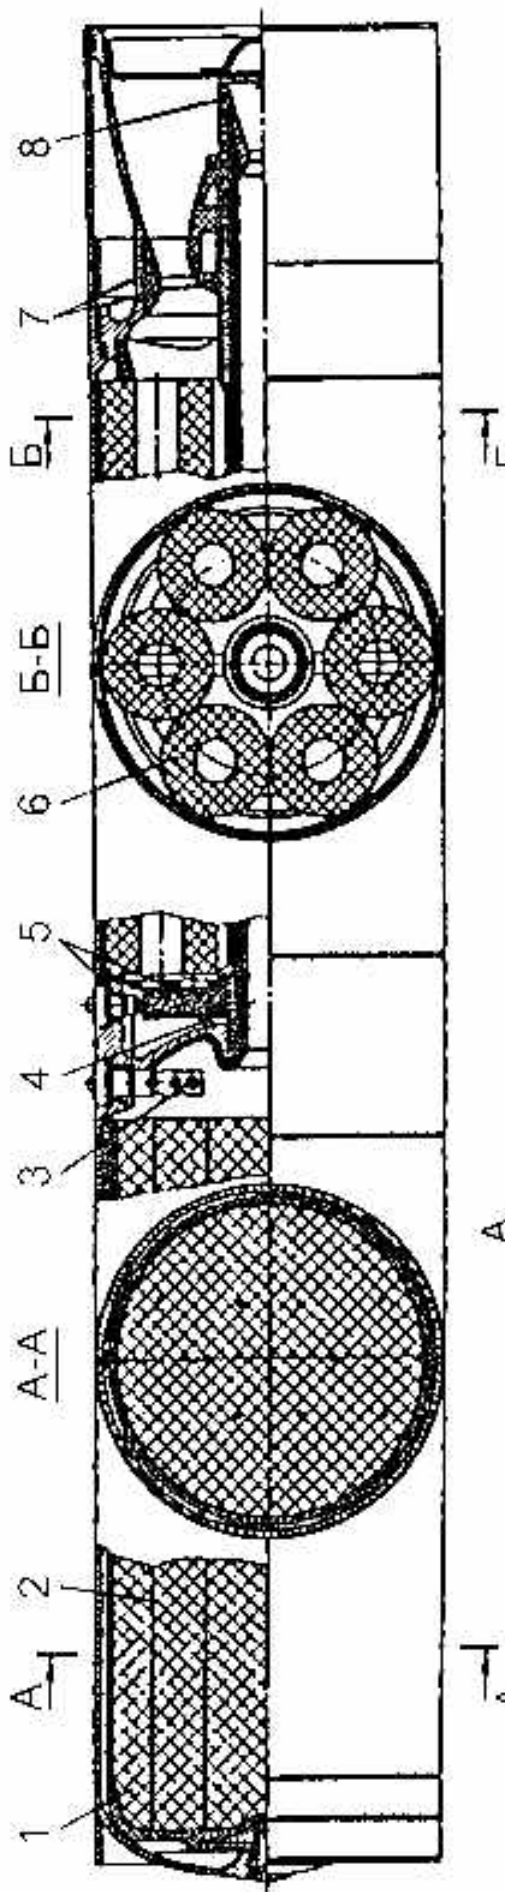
Дворежимний двокамерний РДТП з газоводом:
